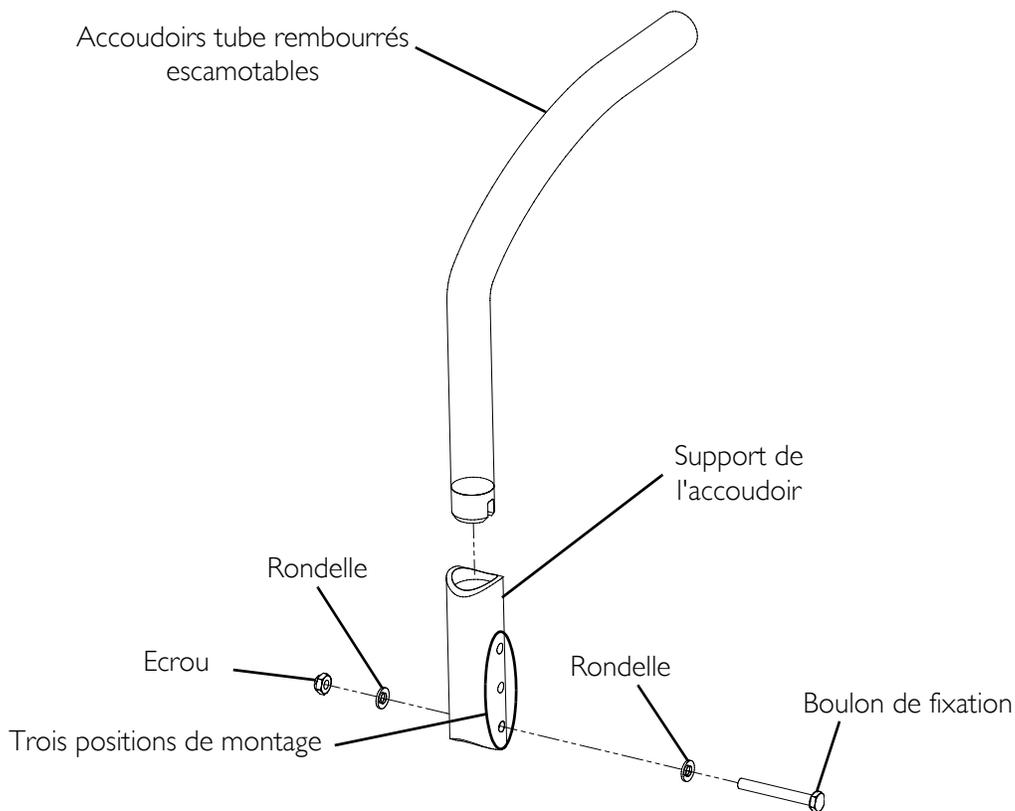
Régler la hauteur de l'accoudoir tube rembourré escamotable
